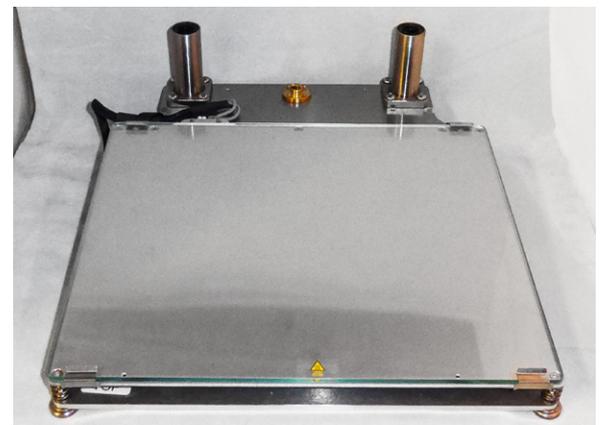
Solide Konstruktion – Druckbett mit Heizung, Glasplatte und Dreipunktnivellierung
